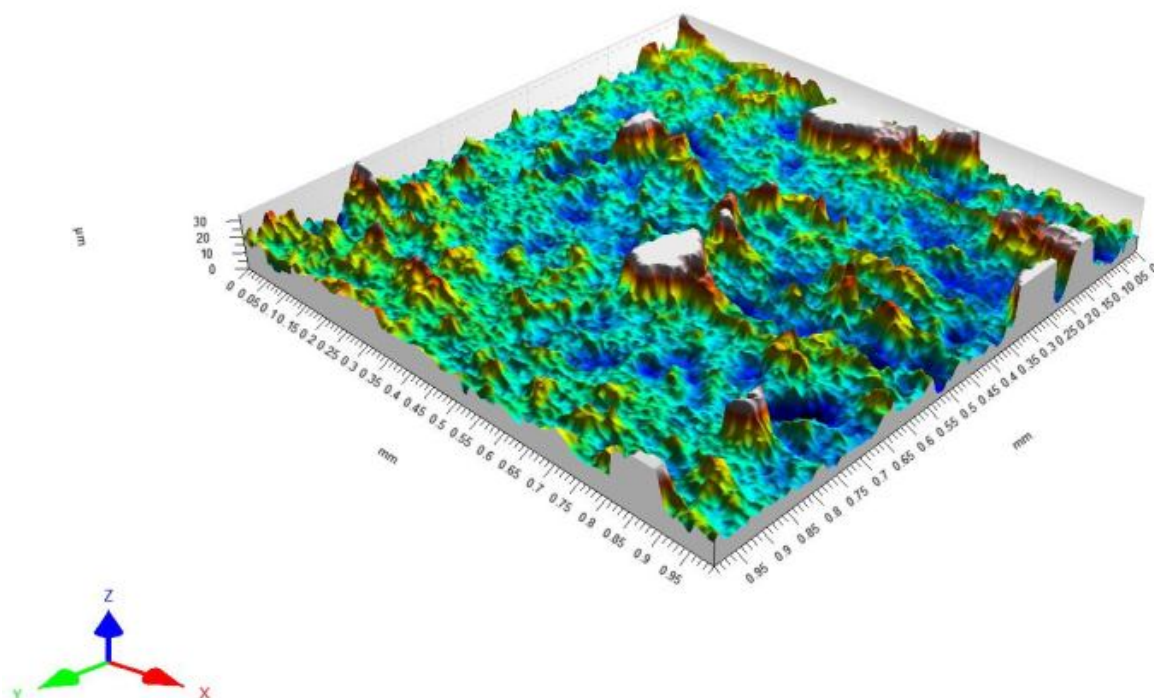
3D zobrazení broušeného povrchu oceli 19 436
